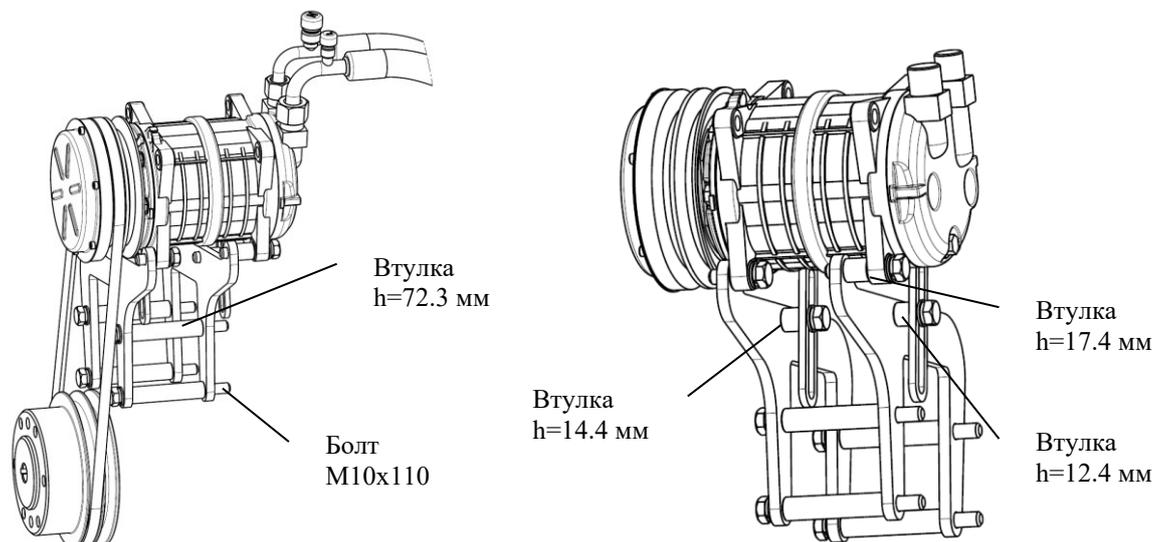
Сборка кронштейна компрессора для трактора Беларусь-890, 920, 950.
